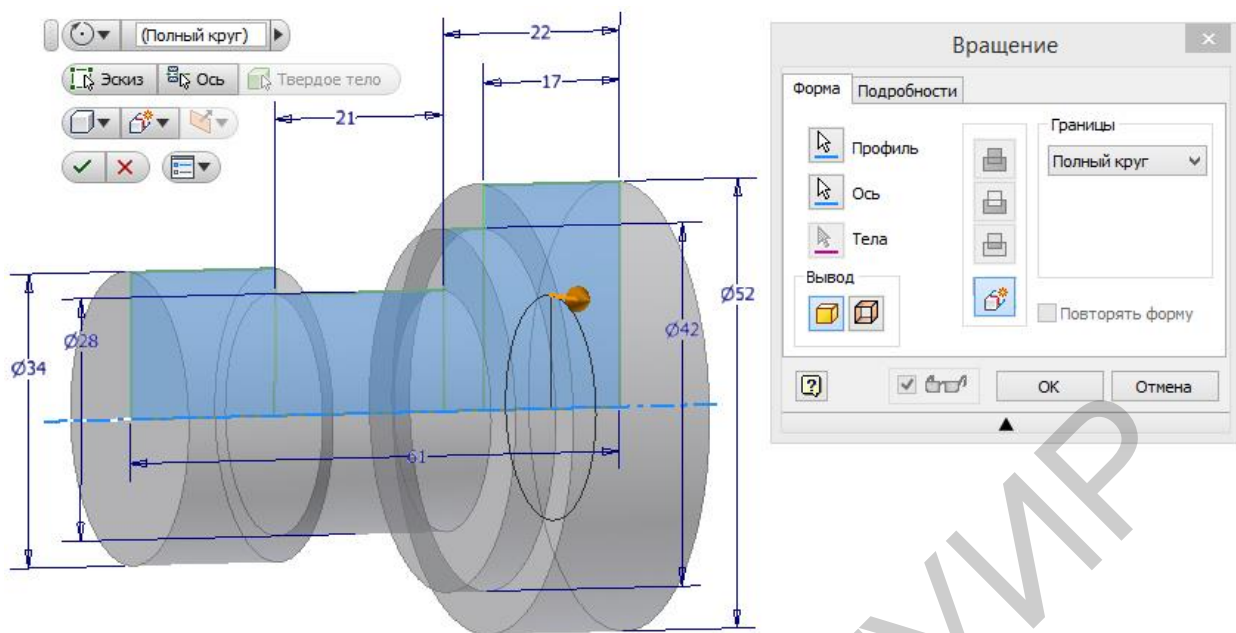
Первая стадия формообразования заготовки корпуса
